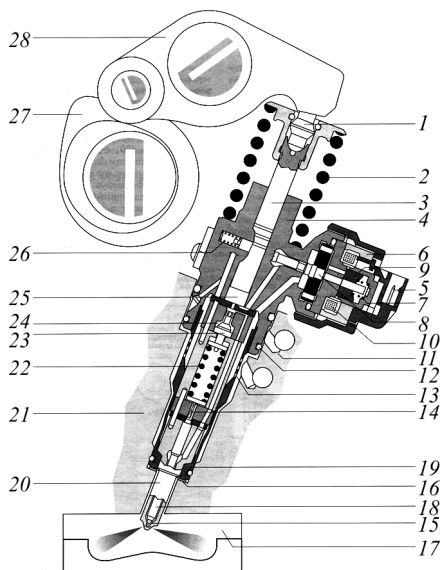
Насос-форсунка: 1 – упор сферический; 2 – пружина возвратная; 3 – плунжер насоса; 4 – корпус; 5 – штекер для подачи управляющего сигнала; 6 – сердечник электромагнита; 7 – пружина выравнивающая; 8 – игла соленоидного клапана; 9 – якорь электромагнита; 10 – катушка электромагнита; 11 – канал обратного слива топлива; 12 – уплотнение; 13 – отверстия-фильтры подвода топлива; 14 – гидроупор; 15 – седло иглы; 16 – шайба уплотнительная; 17 – камера сгорания; 18 – игла распылителя; 19 – гайка распылителя; 20 – распылитель; 21 – головка блока; 22 – пружина распылителя; 23 – уравнивающий поршень; 24 – полость аккумулярования топлива; 25 – полость высокого давления; 26 – пружина электромагнитного клапана; 27 – вал привода насос-форсунки; 28 – коромысло
